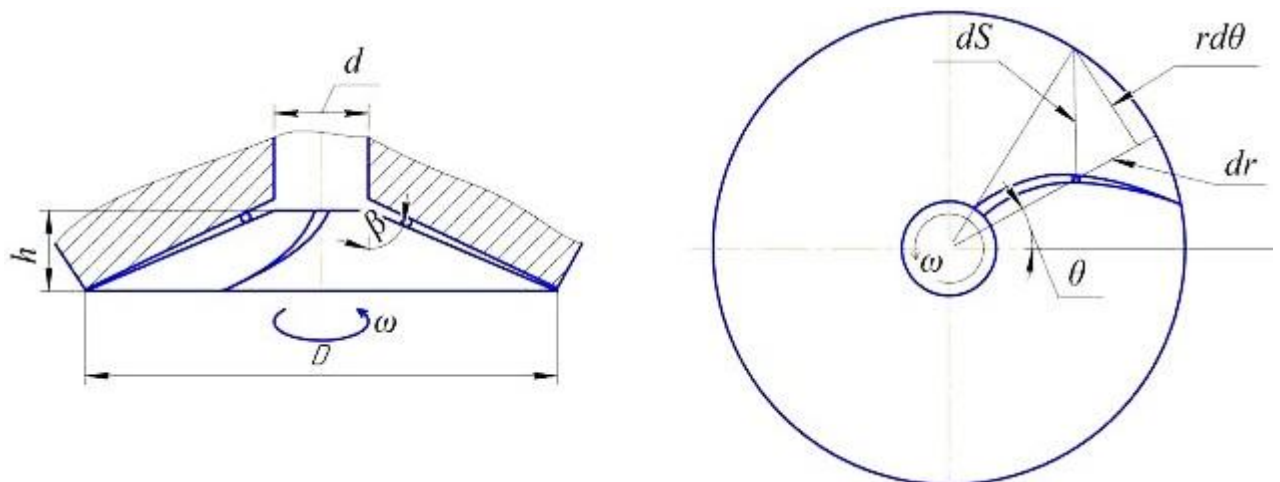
Кінематична схема руху зерна по абразивній поверхні диска з
